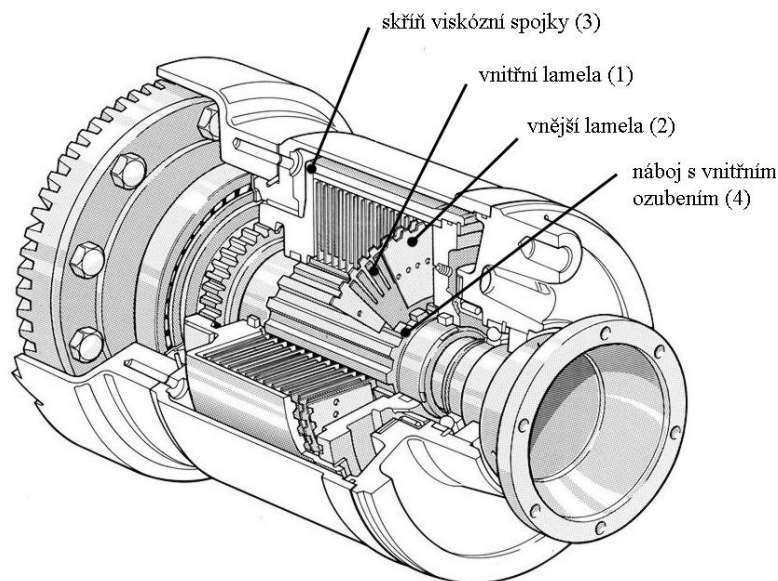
Typy diferenciálu s viskózní spojkou [31]
